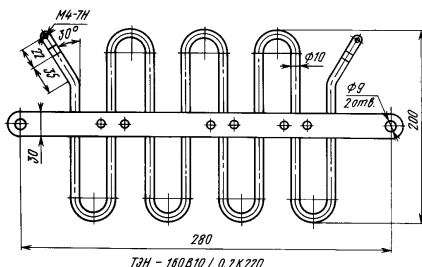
Габаритные, установочные и присоединительные размеры ТЭНа 160В10/0,2К220
